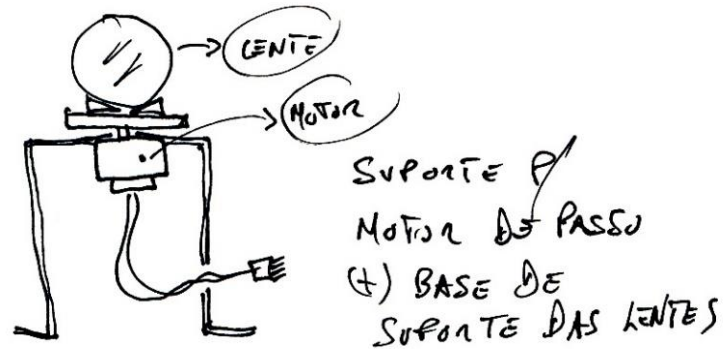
Esboço para suporte do motor de passo e mecanismo de lentes e filtros
